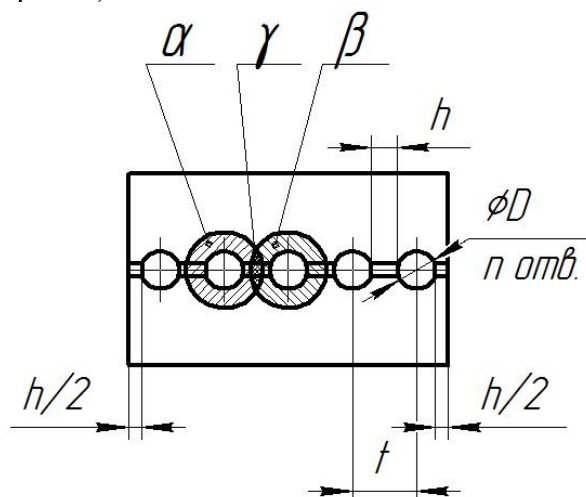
Схема подготовки дефектной детали к ремонтной заварке путём сверления отверстий вдоль траектории трещины и схема их заварки с перекрытием
